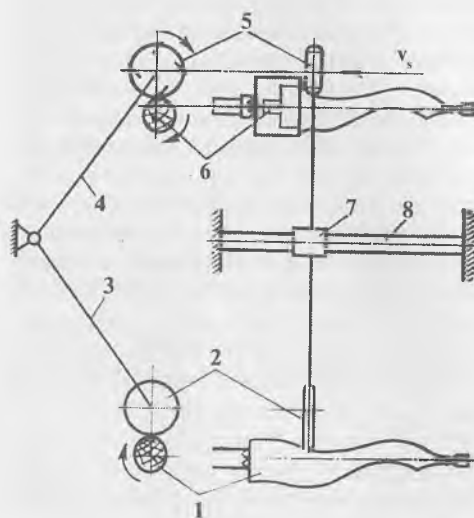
Схема объемного поперечного копирования на станках с продольной подачей фрезы:
